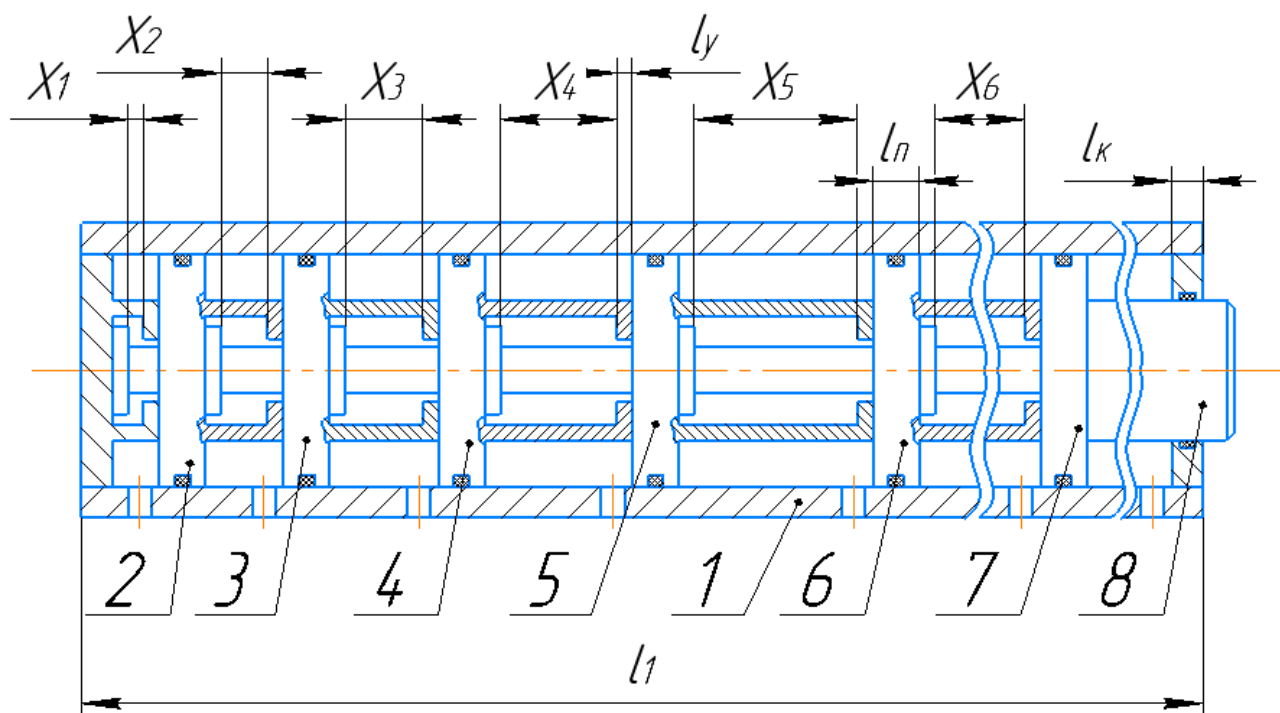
Шестипоршневий багатопозиційний пневматичний привод
